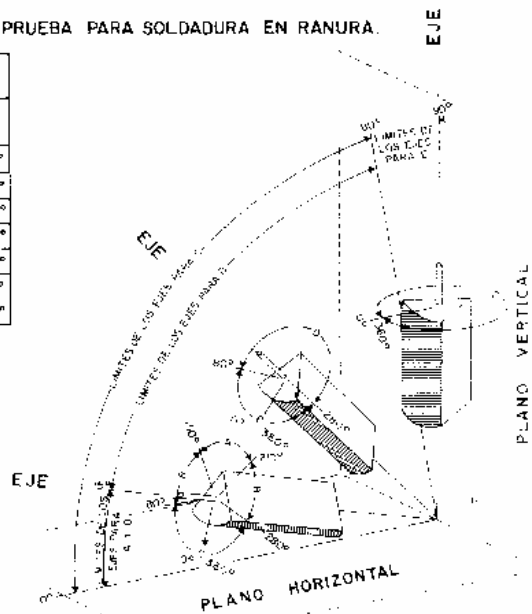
POSICIONES DE LAS PLACAS DE PRUEBA PARA SOLDADURA EN RANURA.
